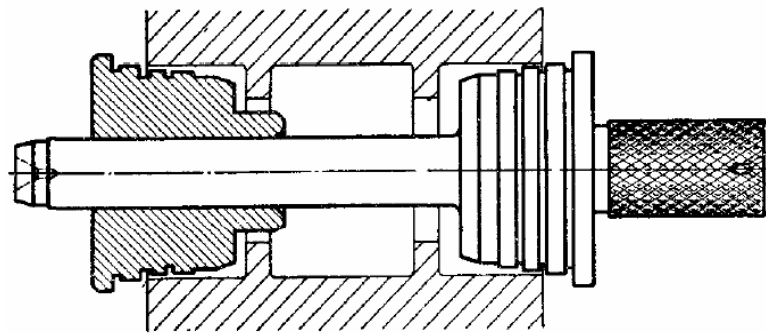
Конструкція ступінчастої циліндричної оправки
